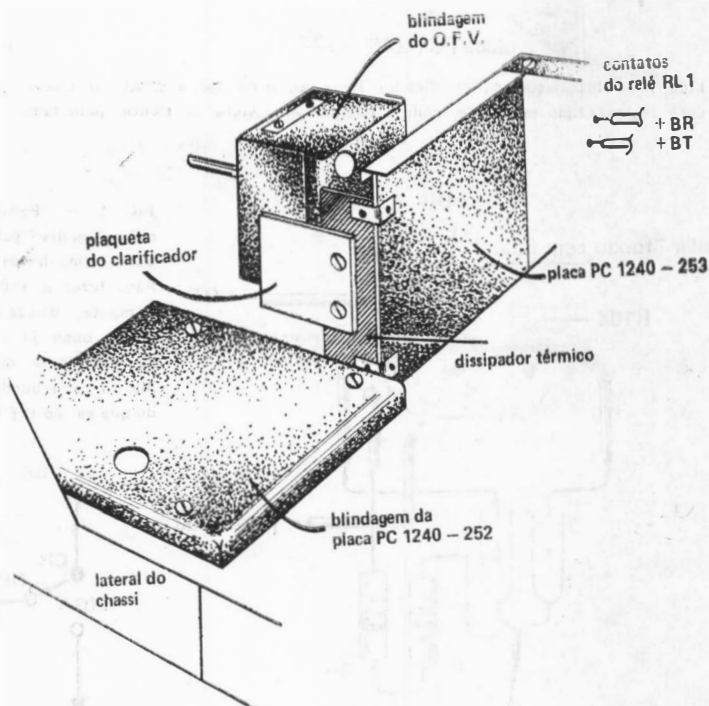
Fixação da plaqueta do clarificador no dissipador de calor. O equipamento é visto por trás e pelo lado esquerdo.
